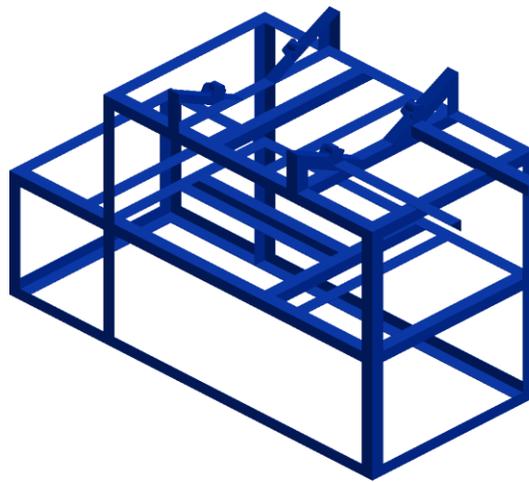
Hasil Desain Mesin Pengering Padi Secara Keseluruhan
